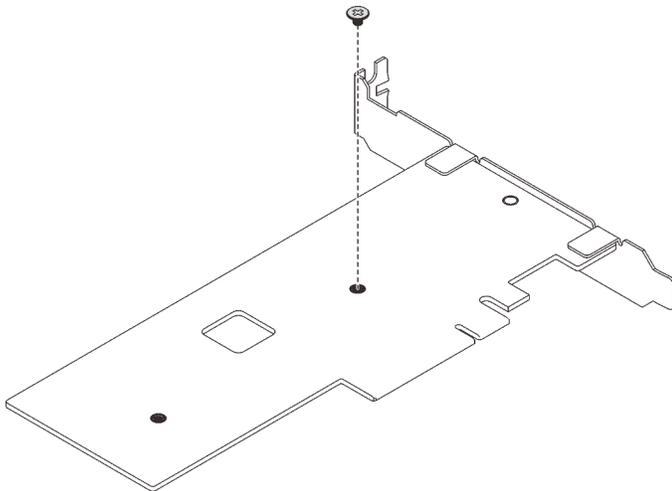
Entfernen der Schraube an der Rückseite des PCIe-Adapters
